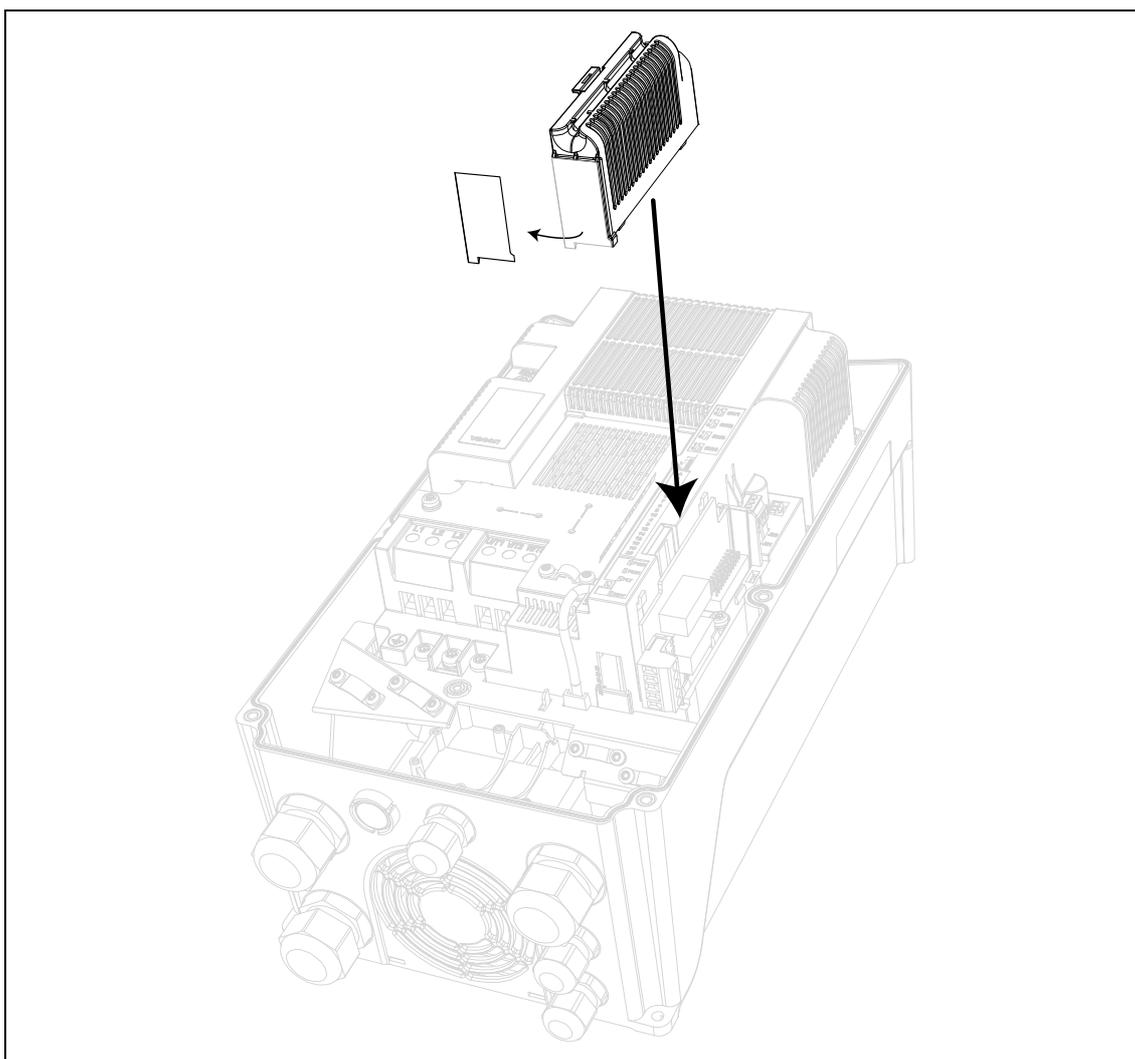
Montaje de la tapa de la ranura opcional: retirar la tapa de plástico para los bornes de la tarjeta opcional.
